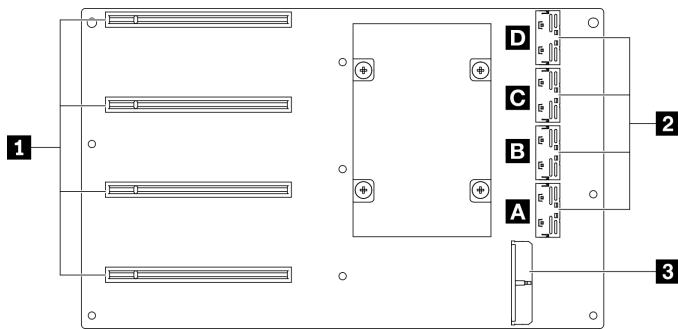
PCIe-Stromversorgungsplatine mit vier umgeschalteten PCIe-x16-Steckplätzen
